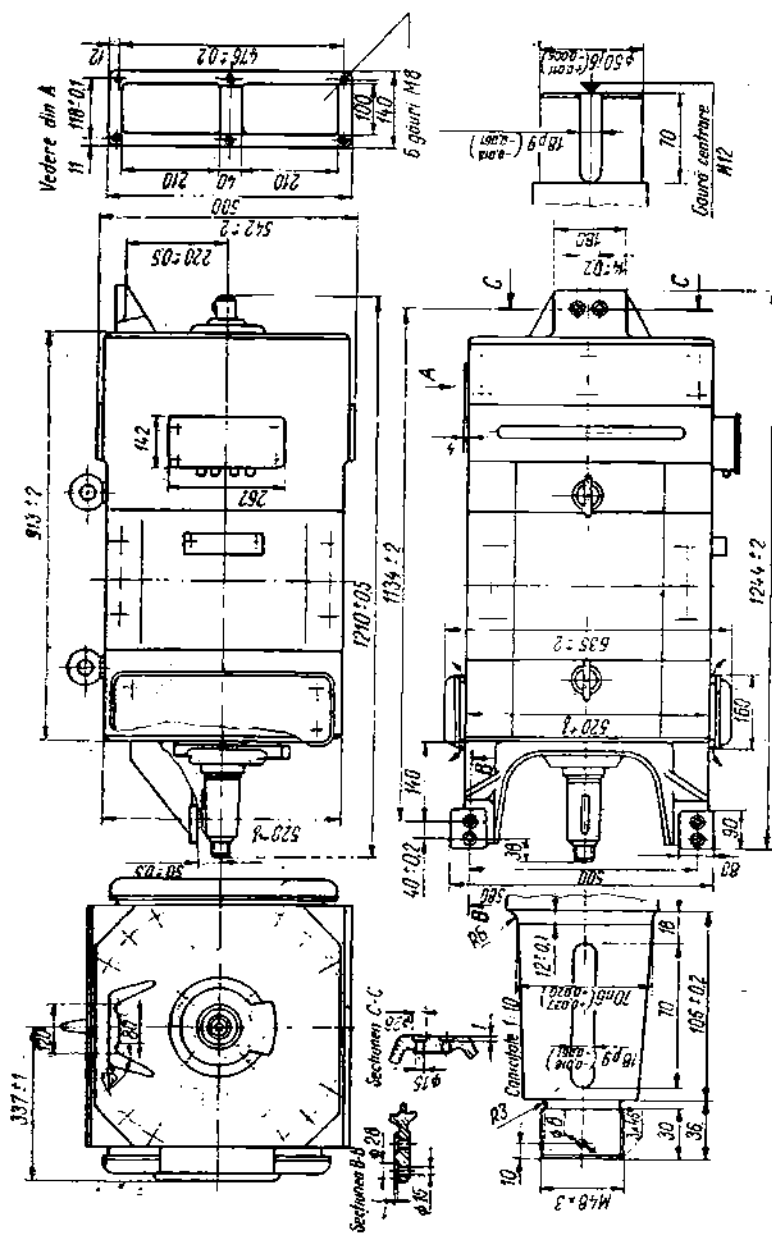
Dimensiunile de gabarit și montaaj ale motorului TN 73.
